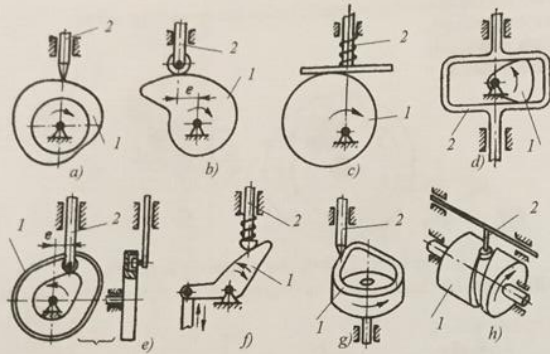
Mecanisme cu camă: a, b, c, d, e, f – came plane; g, h – came spațiale; 1 – camă; 2 – tachtet.
